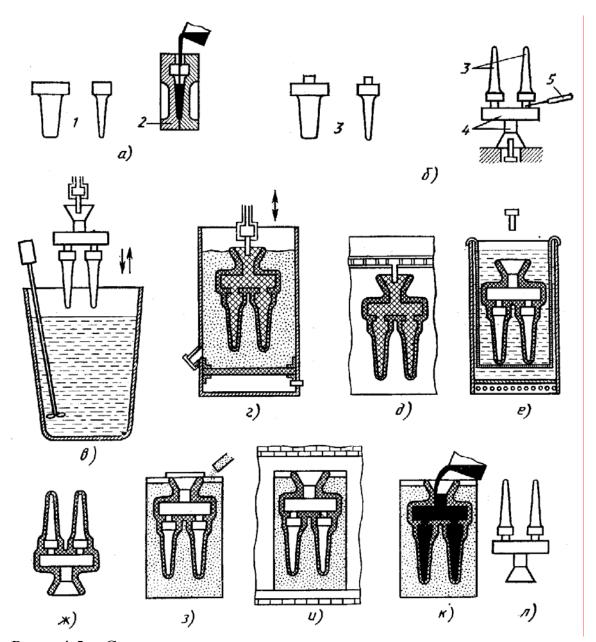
Схема процесса изготовления отливок по выплавляемым моделям.
